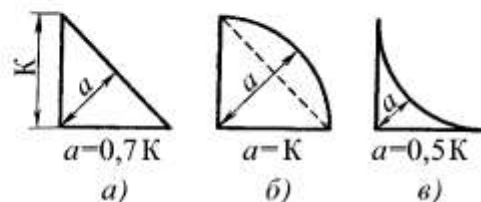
Основные конструктивные элементы валиковых швов:
